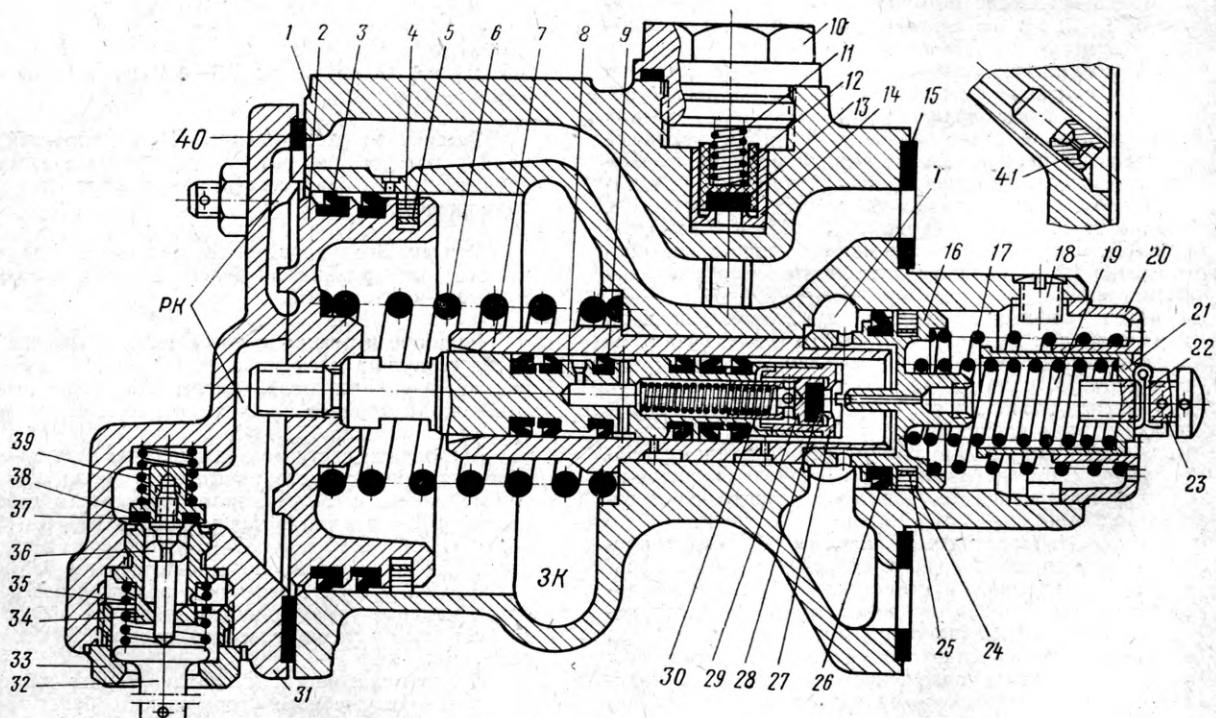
Главная часть усл. № 270-023: 1 — корпус; 2 — главный поршень; 3, 9, 26 — манжеты; 4, 24 — фетровые смазочные кольца; 5 — распорная пружина; 6, 11, 17, 19, 30, 35, 39 — пружины; 7 — втулка; 8 — шток поршня; 10 — заглушка; 12, 29 — клапаны; 13, 28, 38 — уплотнения клапанов; 14, 27, 34 — седла клапанов; 15 — прокладка привалочного клапана; 16 — уравнительный поршень; 18 — винт; 20 — упорка; 21 — упорка регулирующая; 22 — сплинт; 23 — винт регулирующий; 25 — распорная пружина; 31 — крышка; 32 — толкатель; 33 — седло толкателя; 36 — хвостовик клапана; 37 — гнездо клапана; 40 — прокладка крышки; 41 — ниппель
